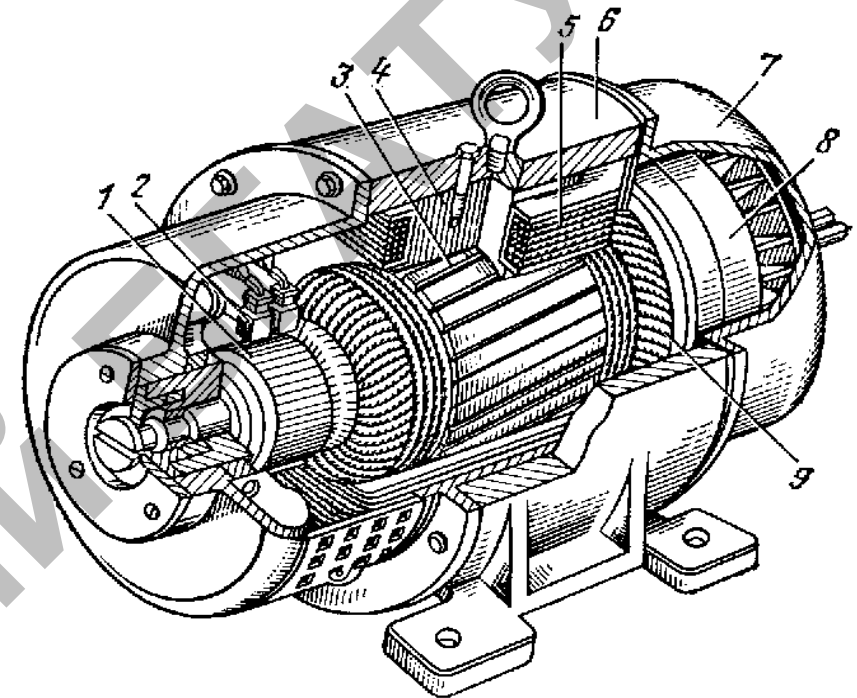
Машина постоянного тока: 1 – коллектор; 2 – щетки; 3 – якорь; 4 – полюс; 5 – обмотка возбуждения; 6 – корпус; 7 – подшипниковые щиты; 8 – вентилятор; 9 – обмотка якоря
